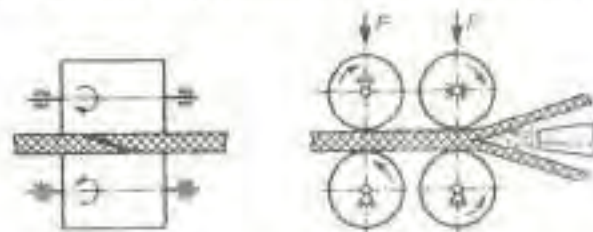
Зварювання нагрітим газом без присадкового матеріалу; F — сила стиску
